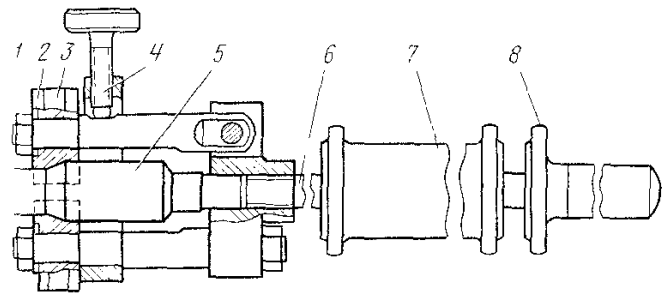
Съемник для снятия первичного вала: 1 — гайка; 2 — пружина; 3 — губки; 4 — винт; 5 — первичный вал; 6 — шпилька; 7 — боек; 8 — ручка
